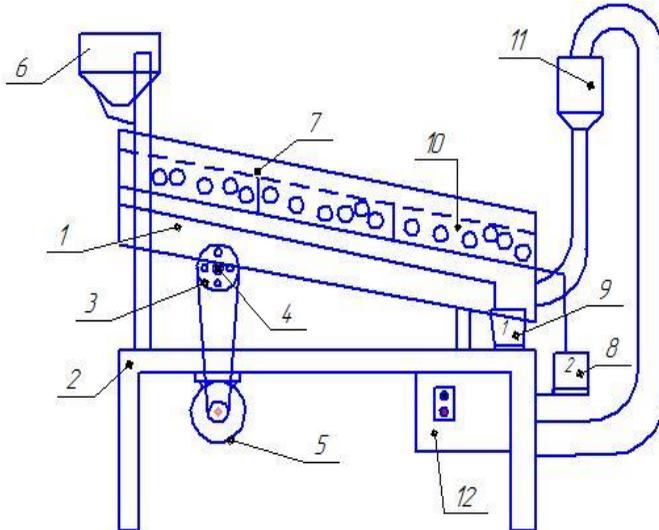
Конструктивная схема сепаратора: 1 - стан решетный; 2 - рама; 3 - передача клиноременная; 4 - вал; 5 - электродвигатель; 6 - бункер; 7 - решето; 8, 9 - лотки; 10 - очиститель шариковый; 11 - очиститель воздушный; 12 - блок управления
